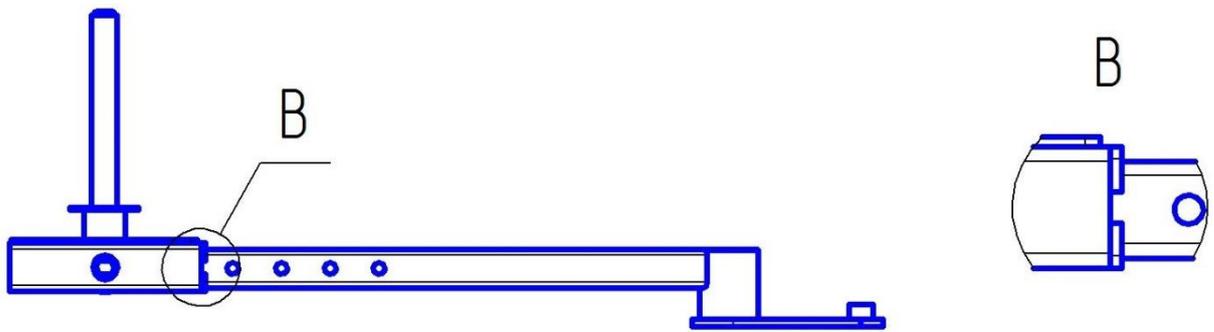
Схема окончательной установки переходника 40x40-50x50.
